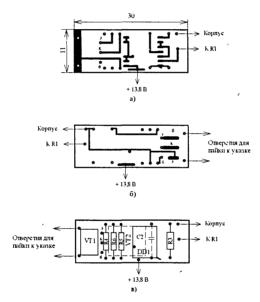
Печатная плата стробоскопа на микросхеме 564ЛЕ5: а — сторона установки DD1; б — сторона установки VT2; в — расположение элементов со стороны установки микросхемы
